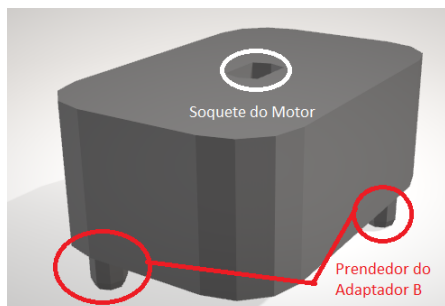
Adaptador B - Adaptador da Bureta com o Motor
